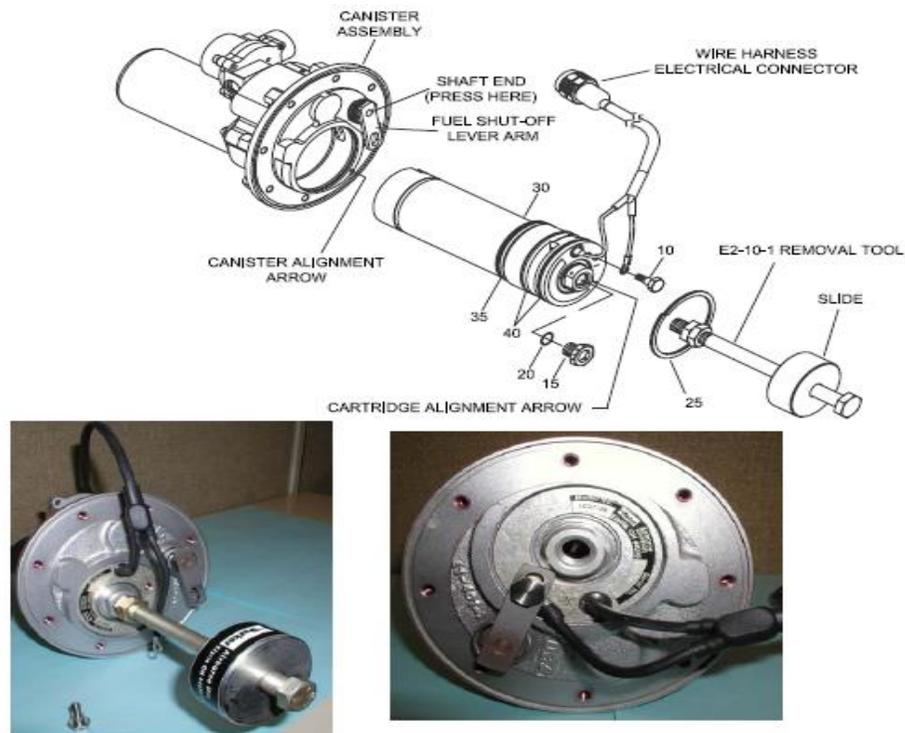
Bomba Auxiliar DC Removible (B)
